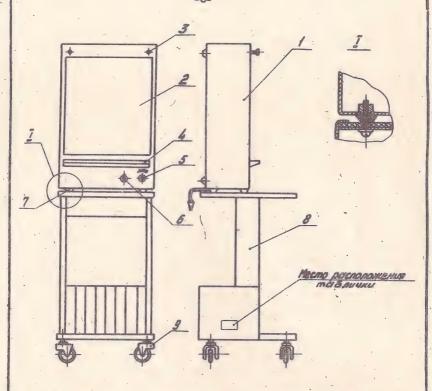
Негатоской общего назначения НТ-48, 1-корпус; 2-экран; 3-кромитейн; 4-желоб; 5-регулятор яркости; 6-выключатель; 7-кож-ка; 8-тележка; 9-колесо.
